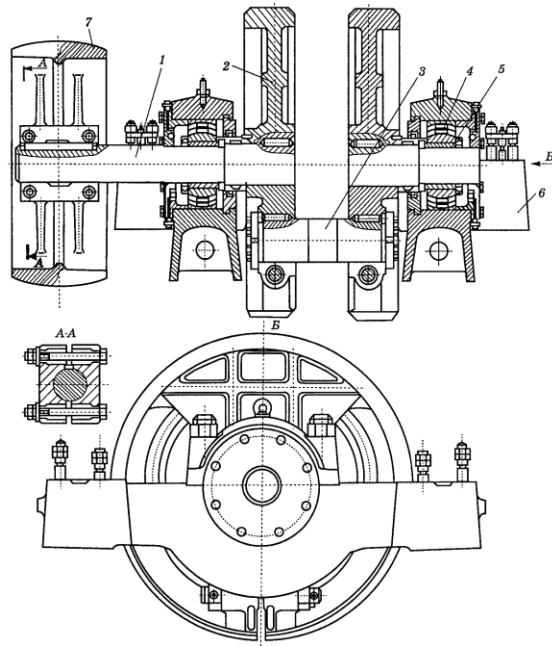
Кривошипний механізм двоповерхової пилорами: 1 – піввал; 2 – маховик; 3 – кривошипний палець; 4 – корінний підшипник; 5 – втулка; 6 – фундаментна плита; 7 – шків плоскопасової передачі
